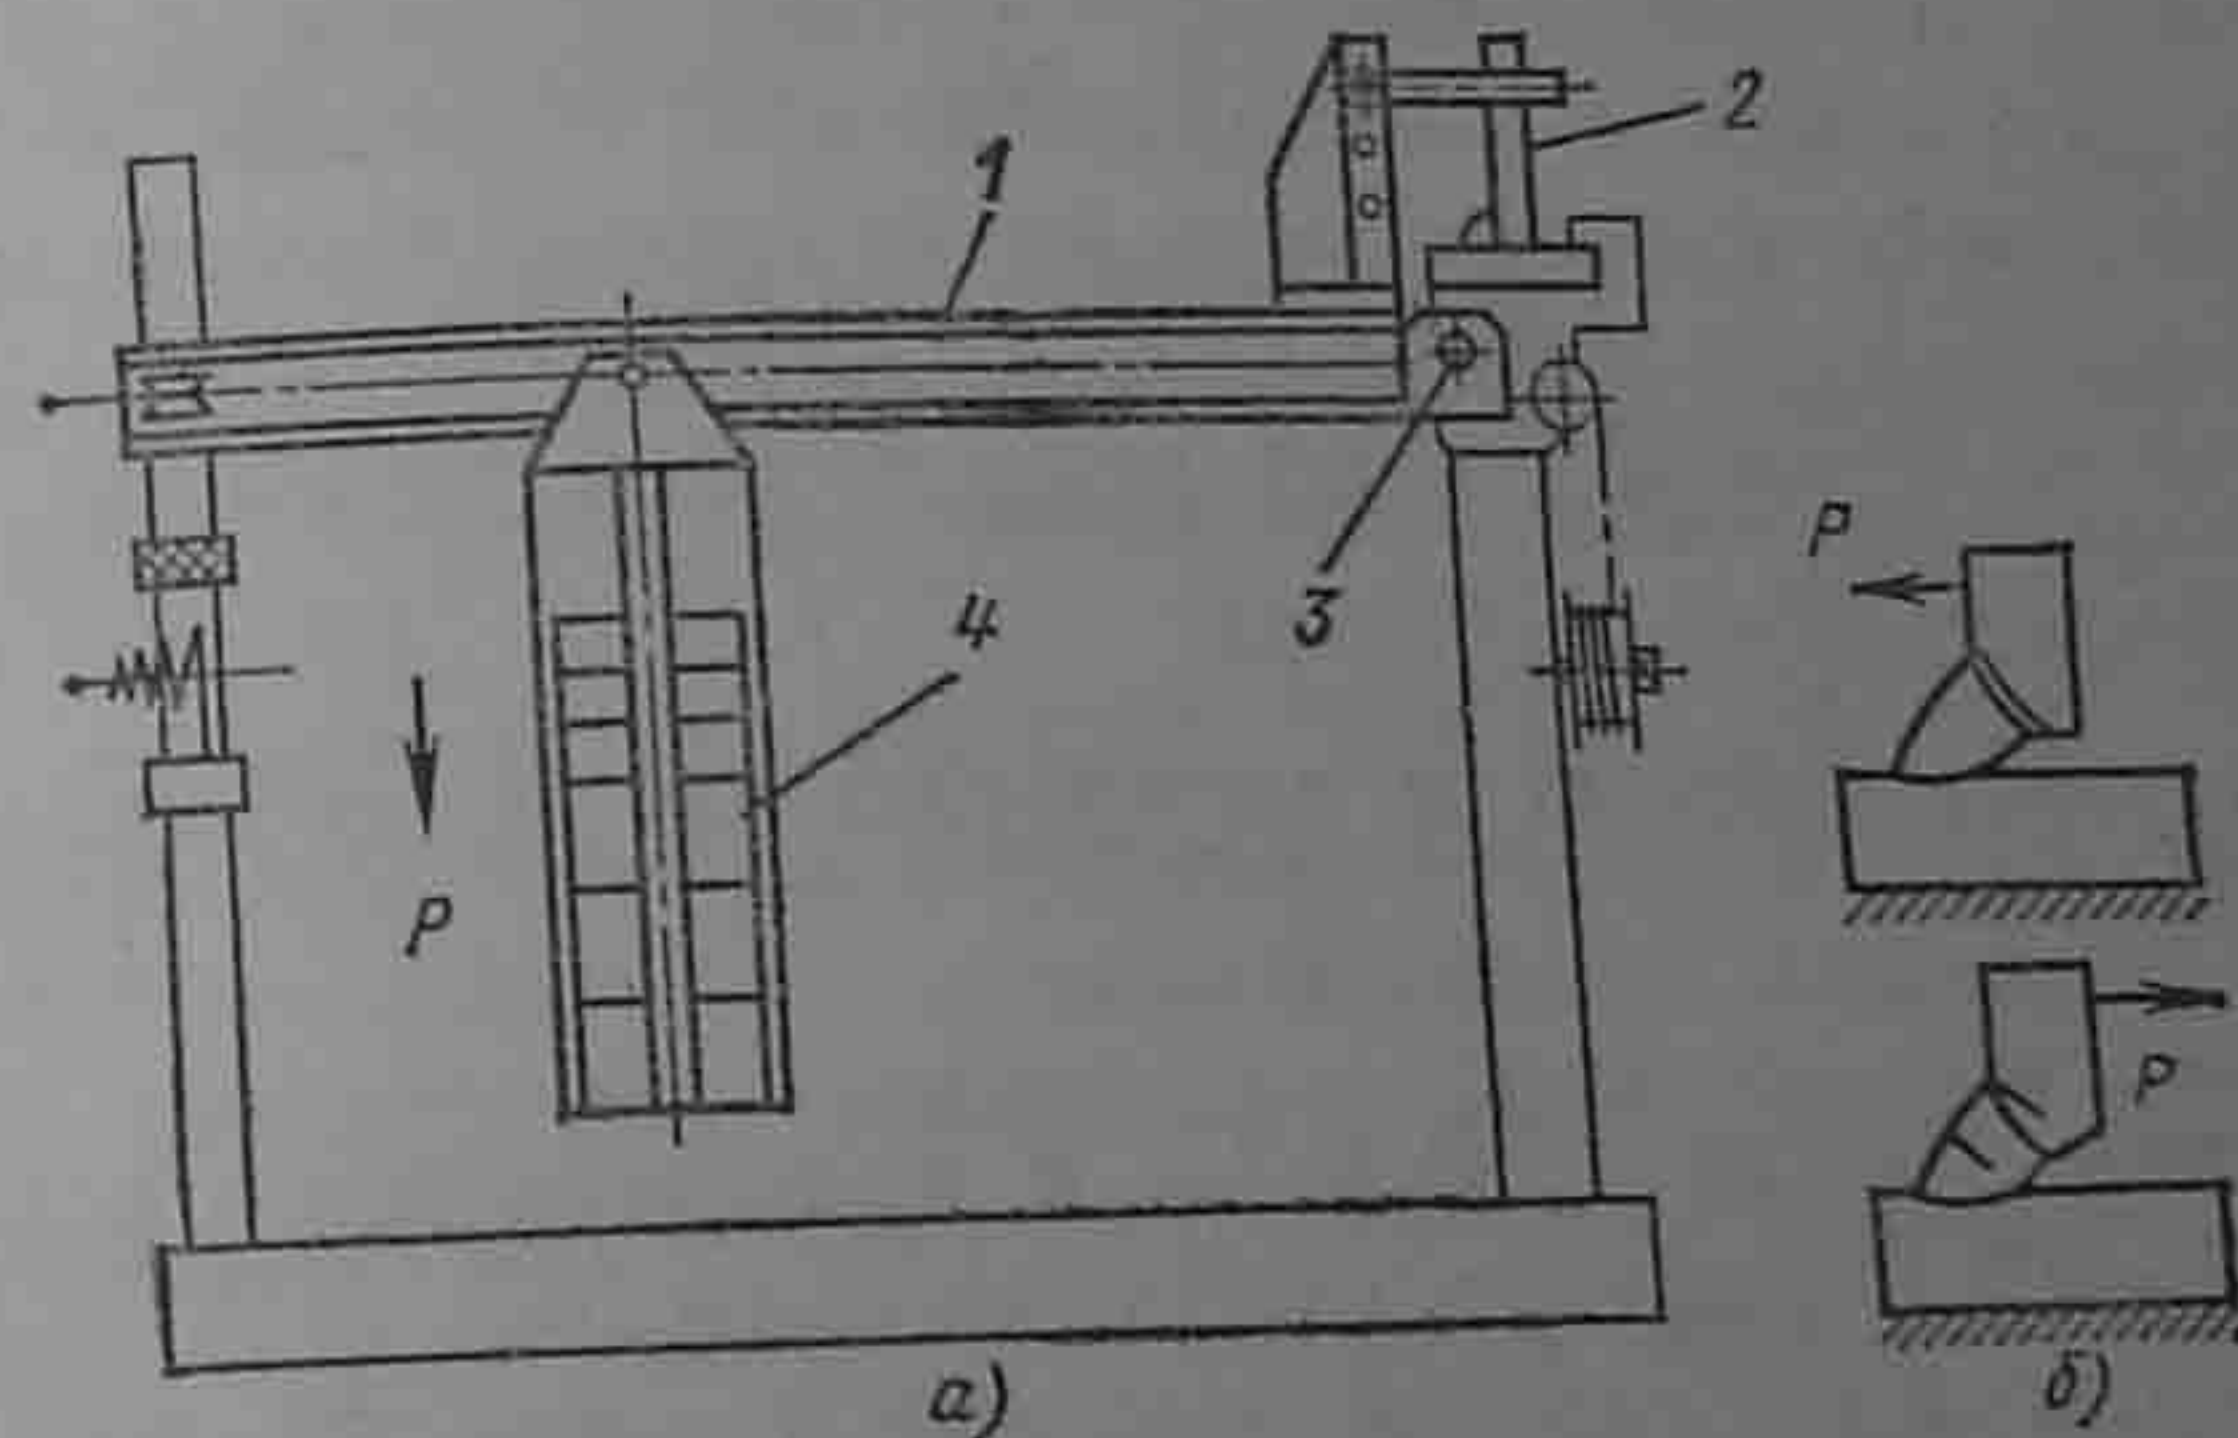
Схема испытательной установки (а) для определения сопротивления сталей образованию холодных трещин при сварке и схема нагружения образца (б):
